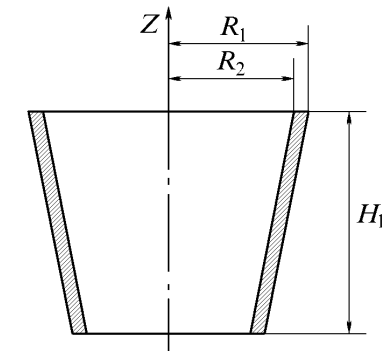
Сечение обрабатываемой тонкостенной цилиндрической детали
